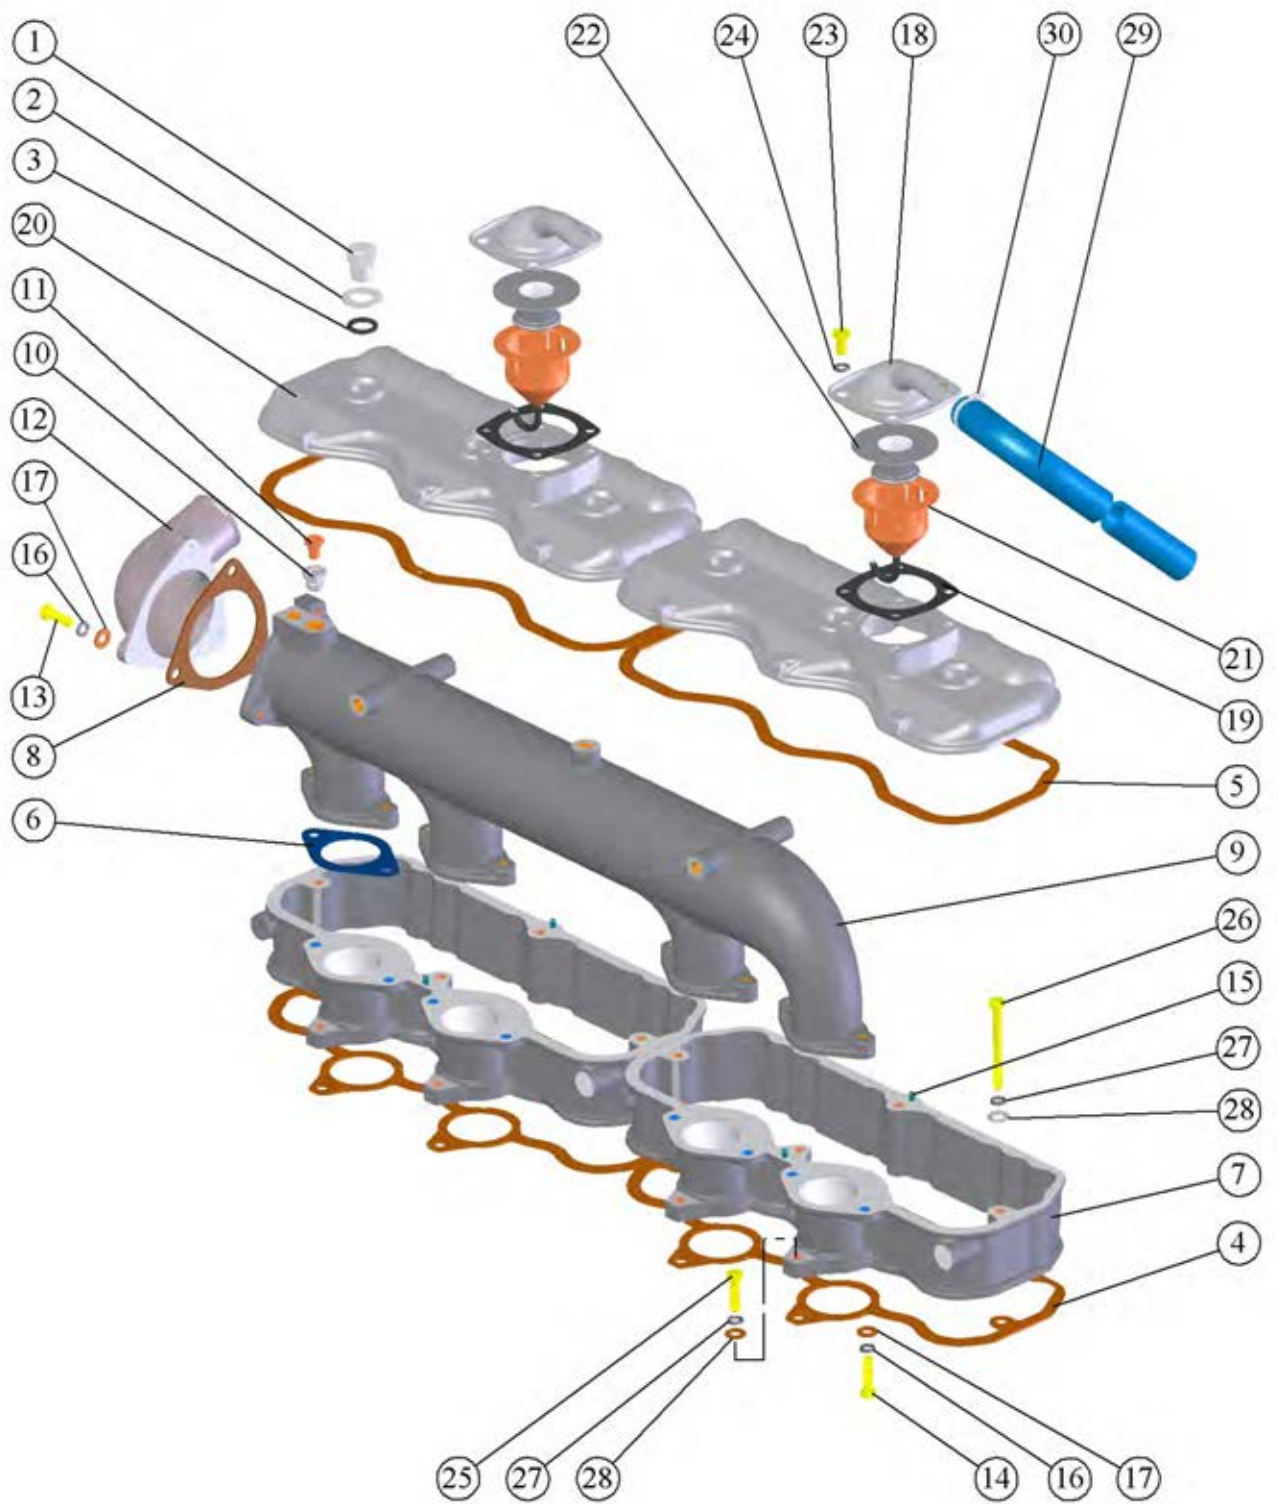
Крышки головок цилиндров, коллектор и сапуны
